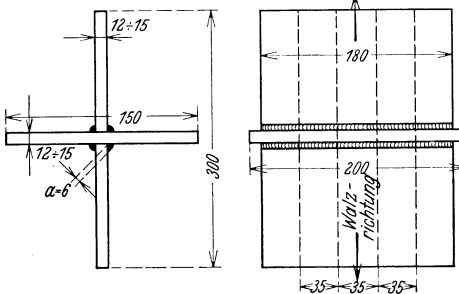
Eckenschweißung für Zug- und Biegeproben nach Skizze zu entnehmen.
